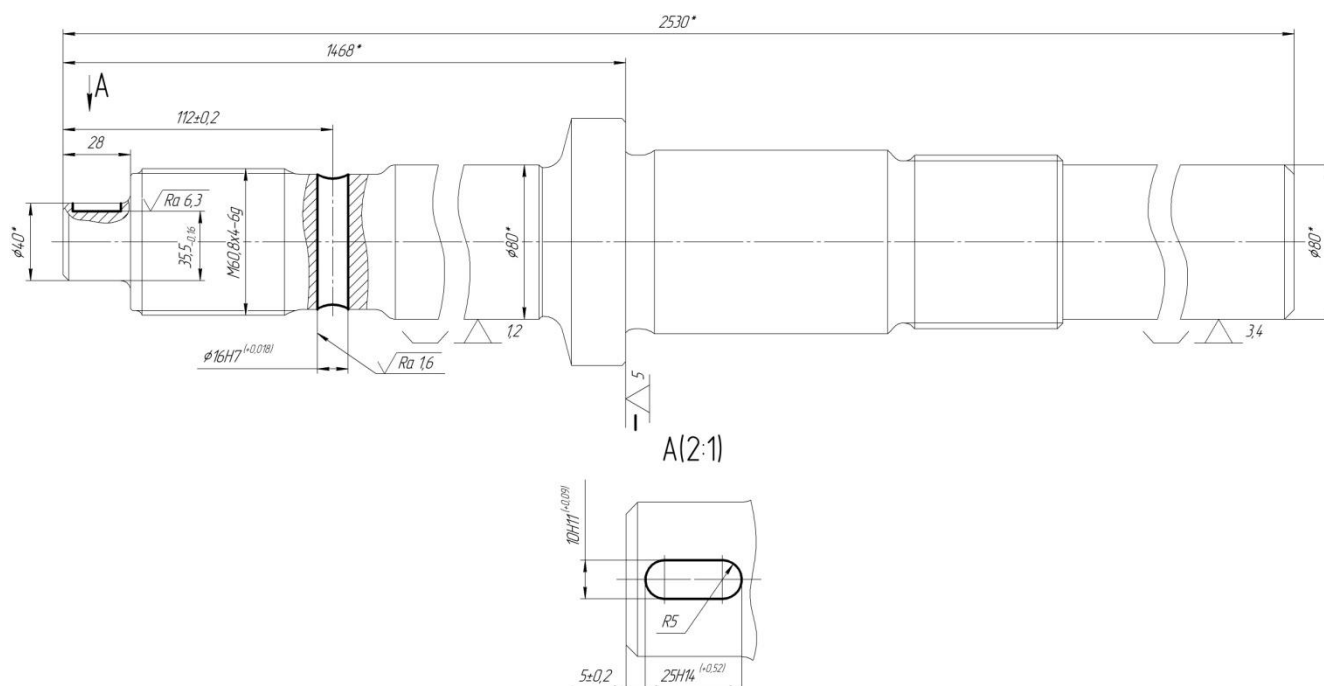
Схема базування заготовки на комплексній з ЧПК операції
